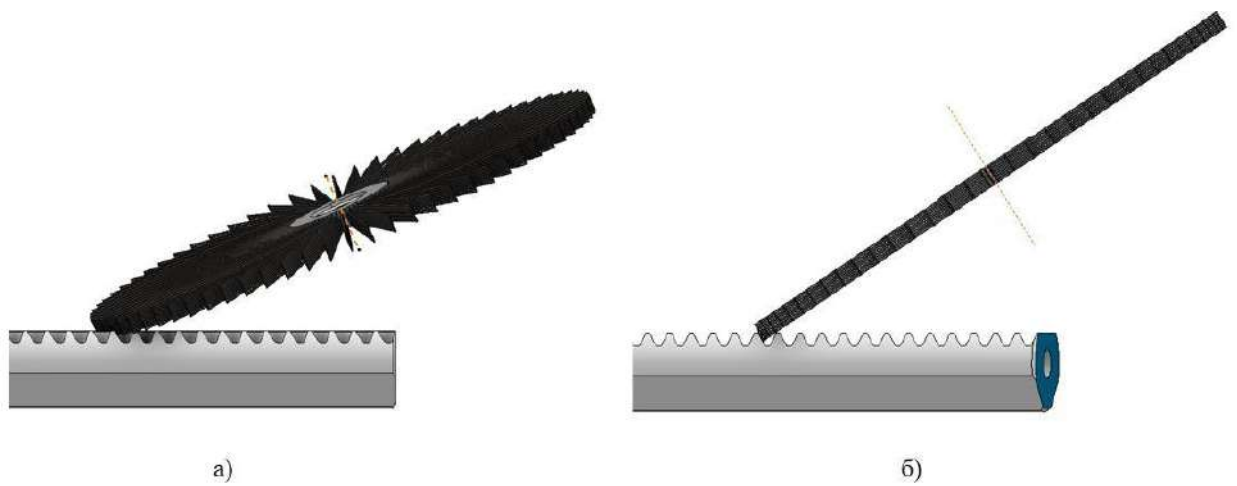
Обробка рульової рейки гнучким інструментом: а – вид збоку; б – вид нормаллю до периферії інструменту
